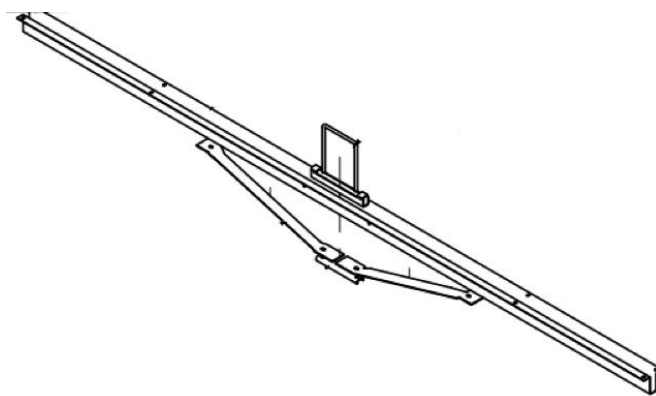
Profilato ad omega trasversale alle strutture ad inseguimento monoassiale
